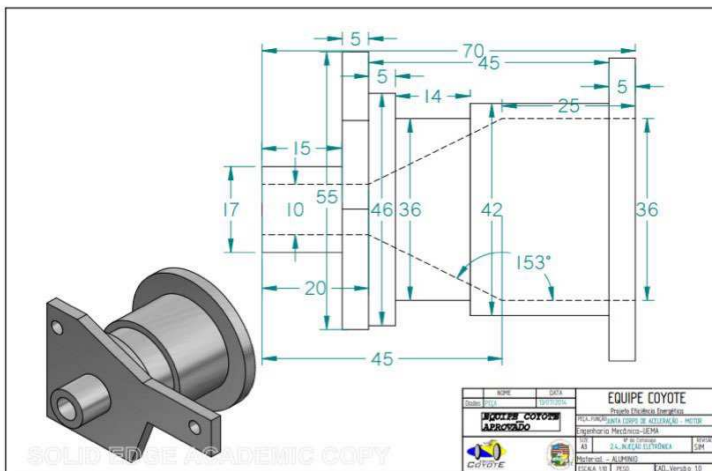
Coletor de Admissão - Equipe Coyote
